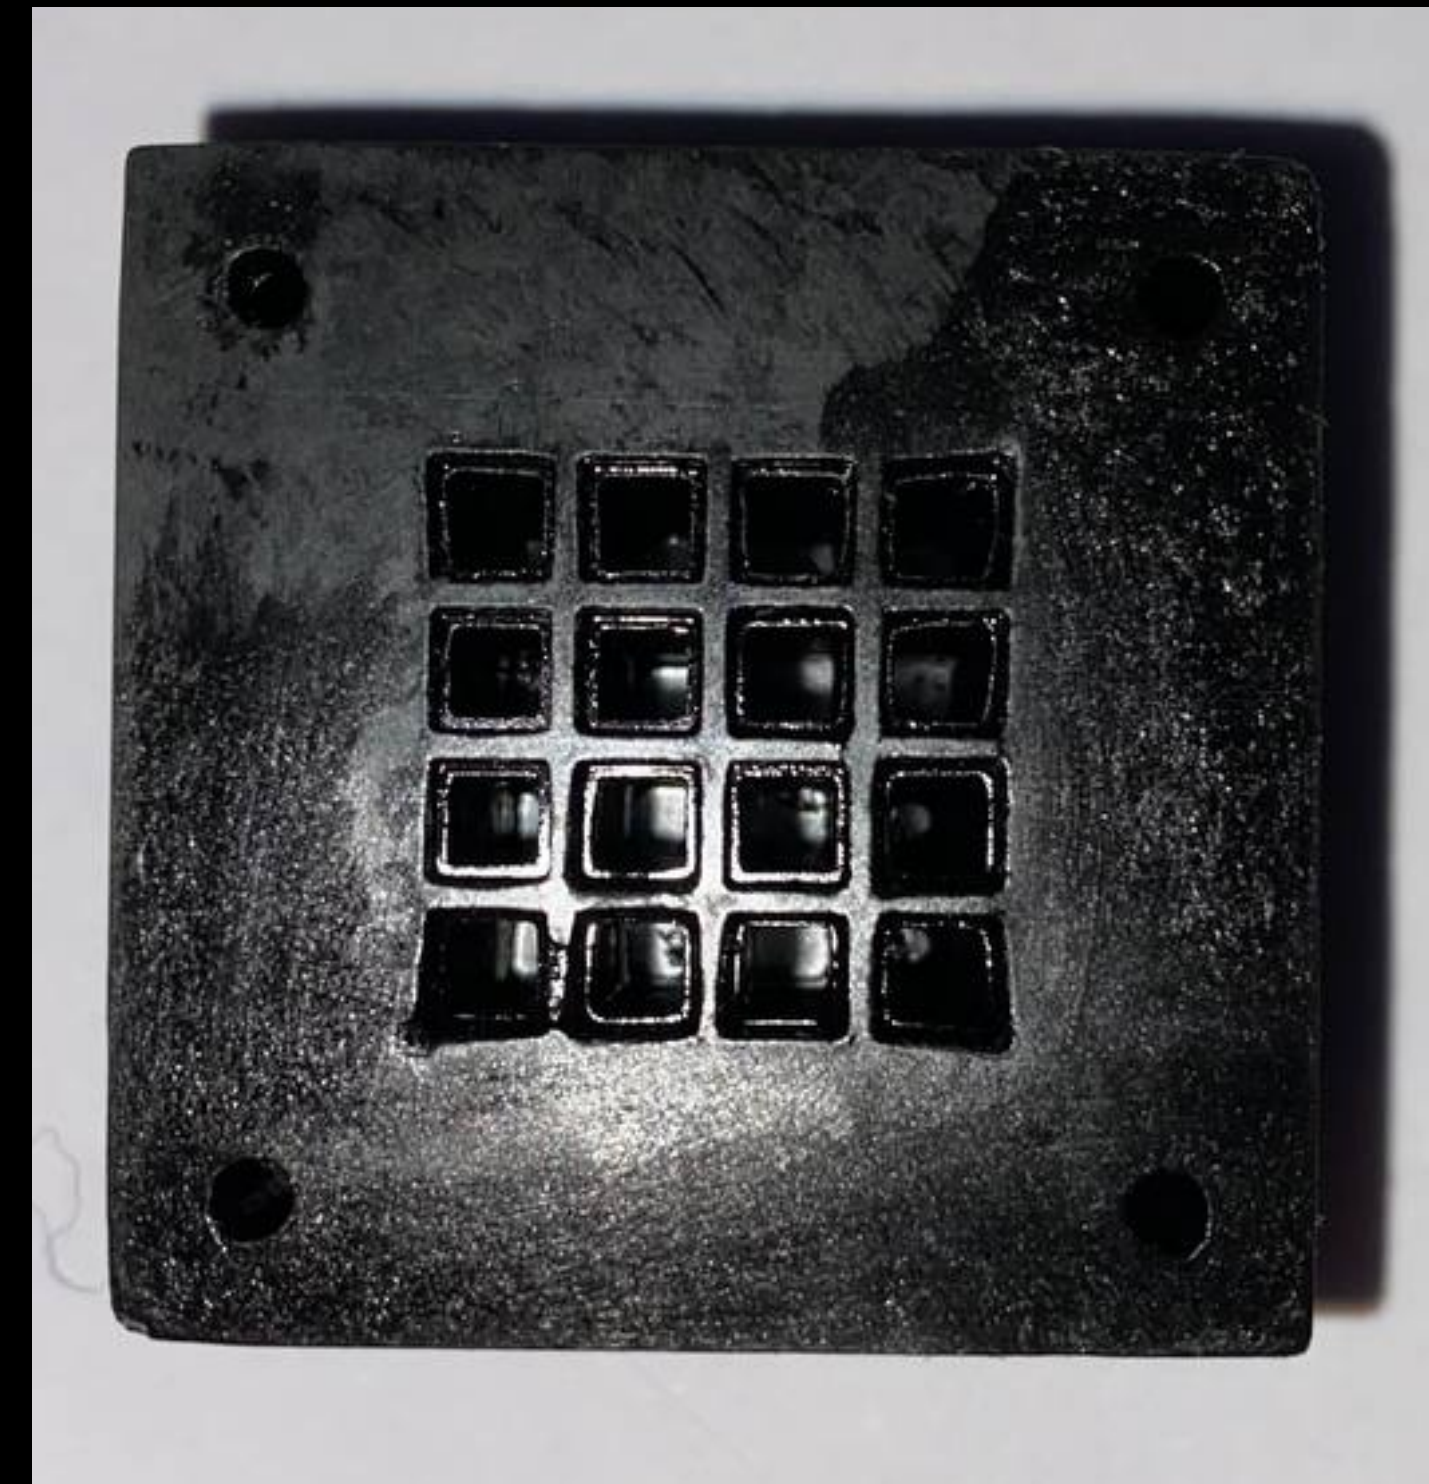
Напечатанный элемент корпуса ПЭТ
